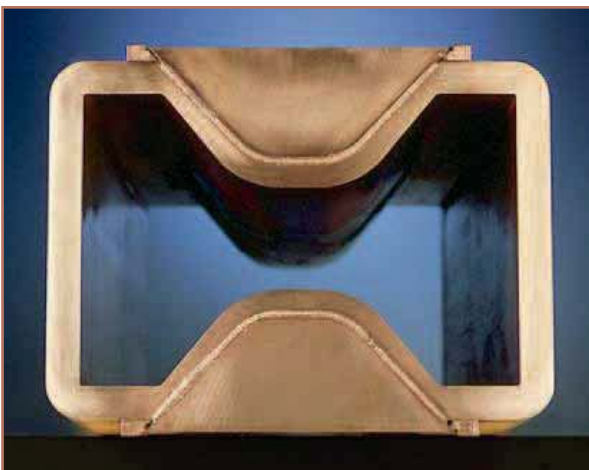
Mit dem Elektronenstrahl eingeschweißte Passtücke an Eingusskokillen aus CuCrZr für die Stahlindustrie (Einschweißtiefe: 40 mm) [56]
